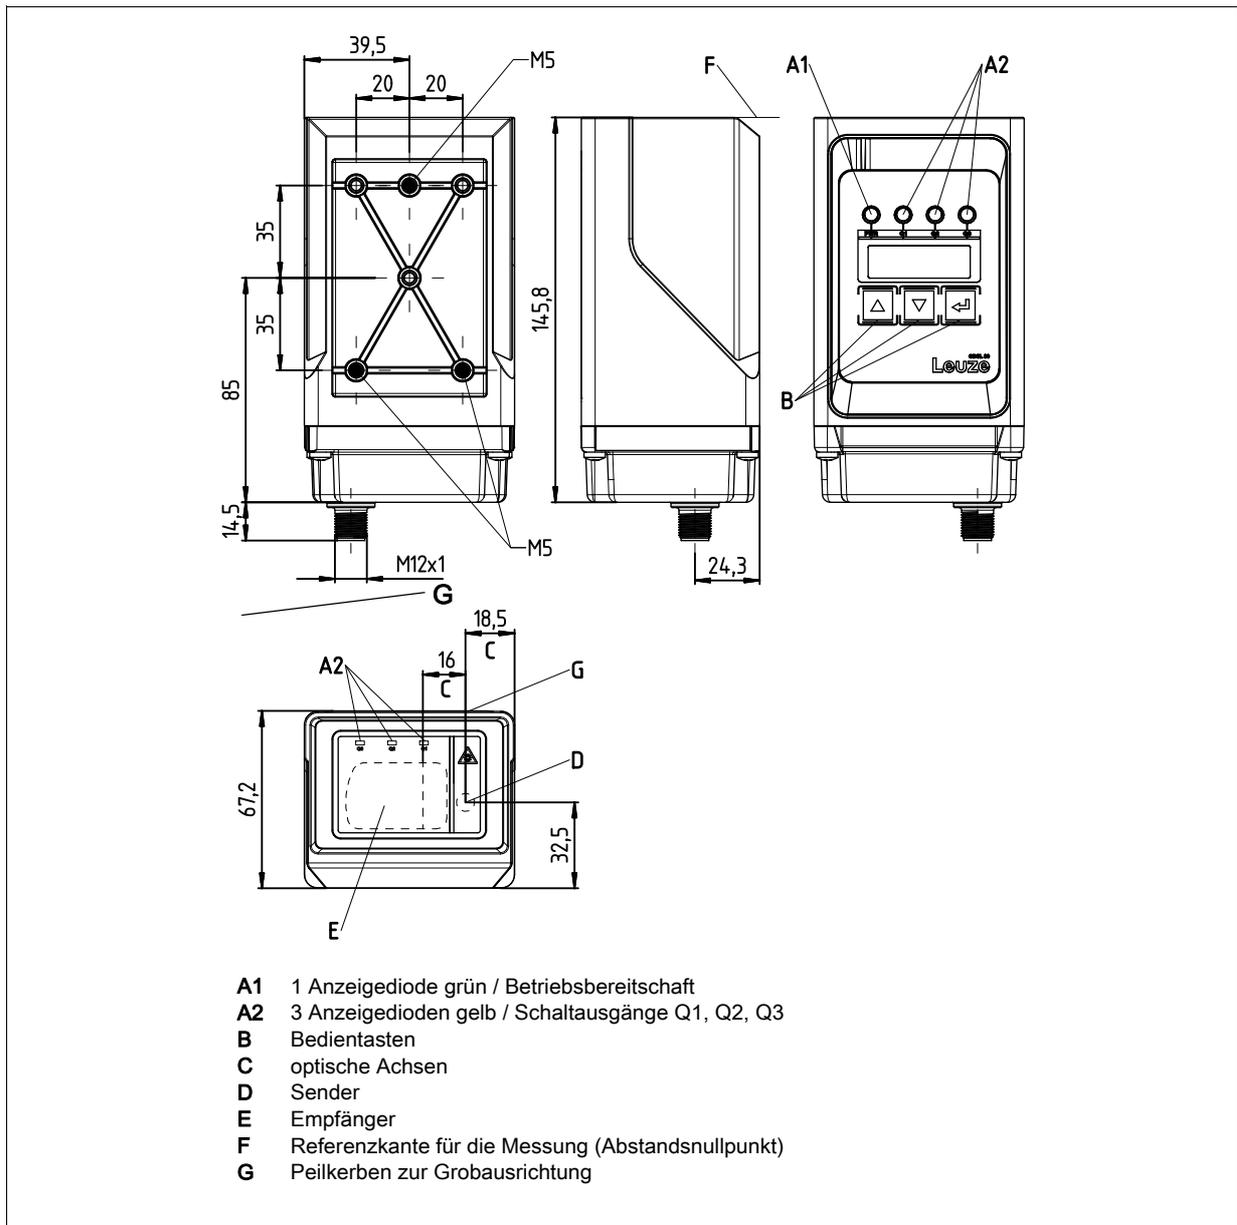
Maßzeichnung ODSL 30 - Typen
